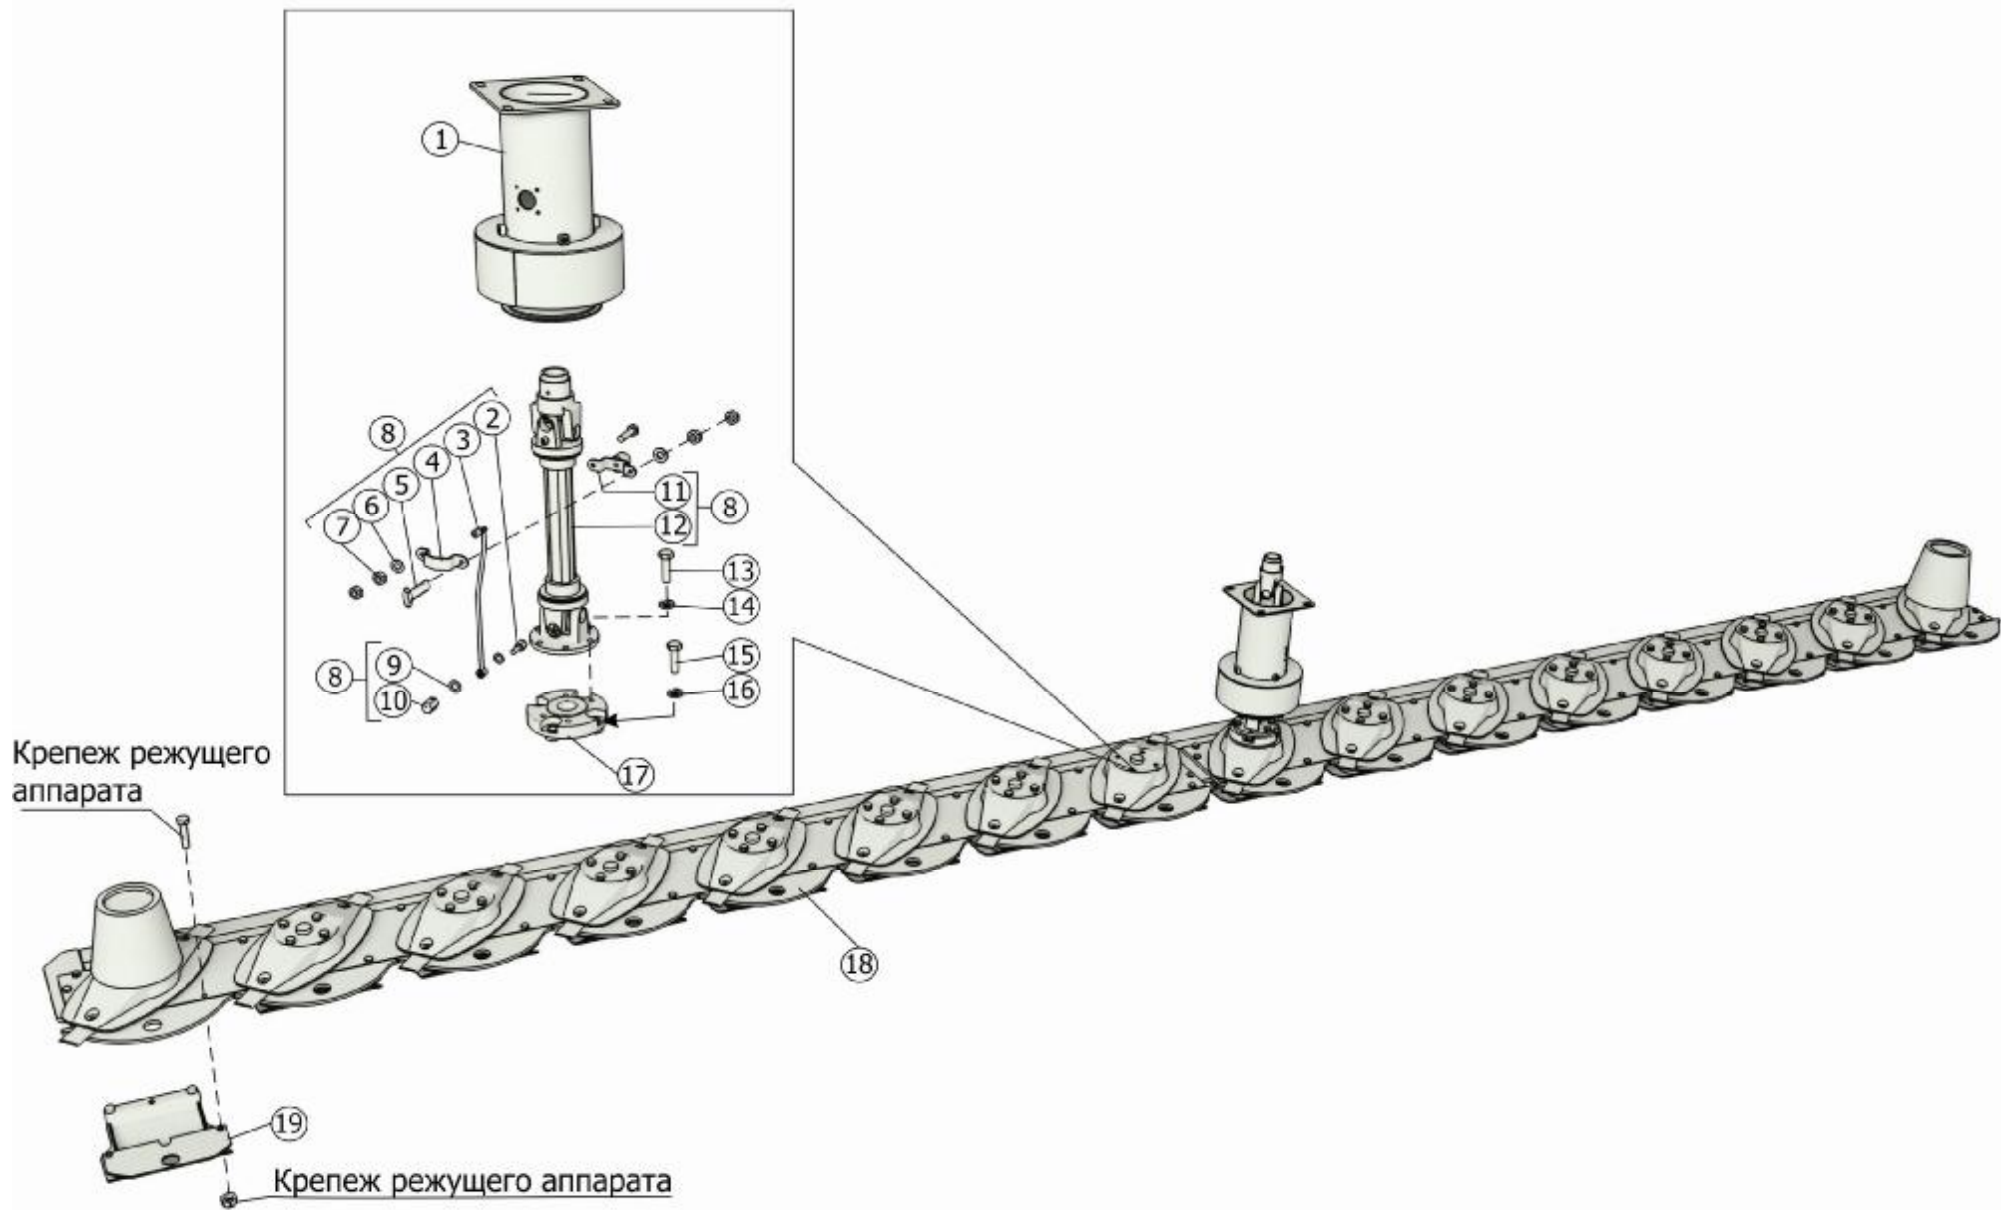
Установка режущего аппарата ЖРН-601.01.05.000
